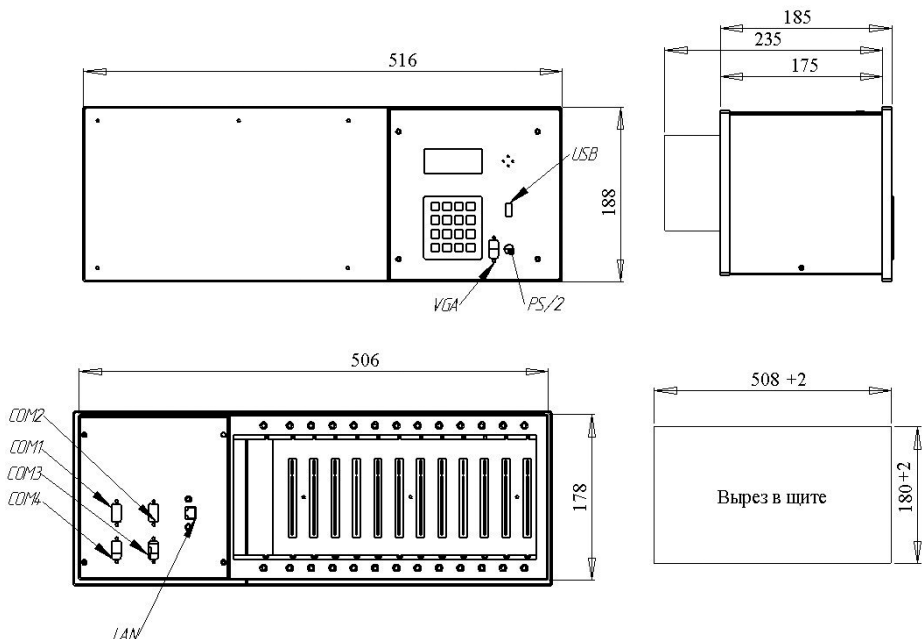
Монтажный чертеж прибора Ш932.7 исп. 022 для щитового монтажа
